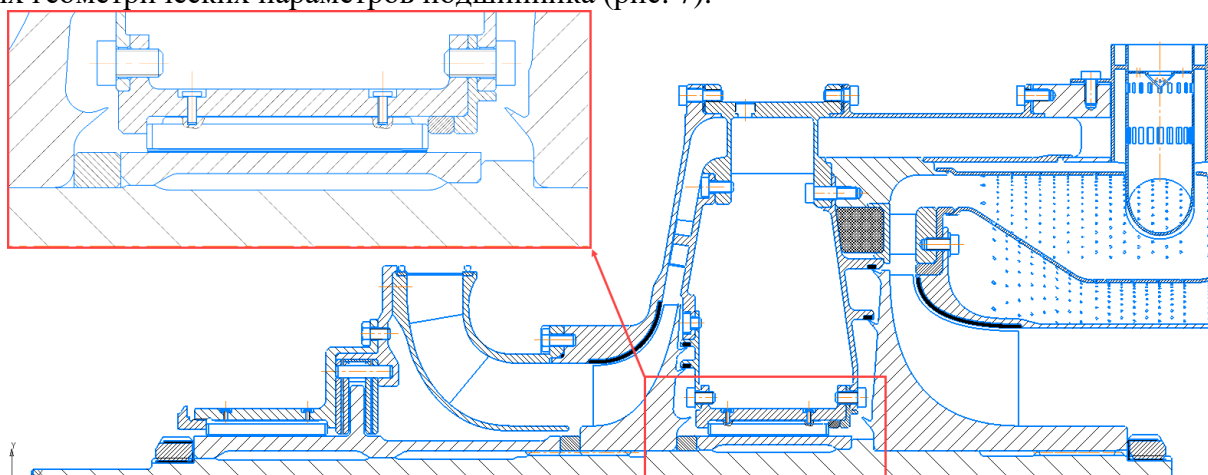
Компоновка малоразмерной газотурбинной установки с газодинамическими подшипниками
